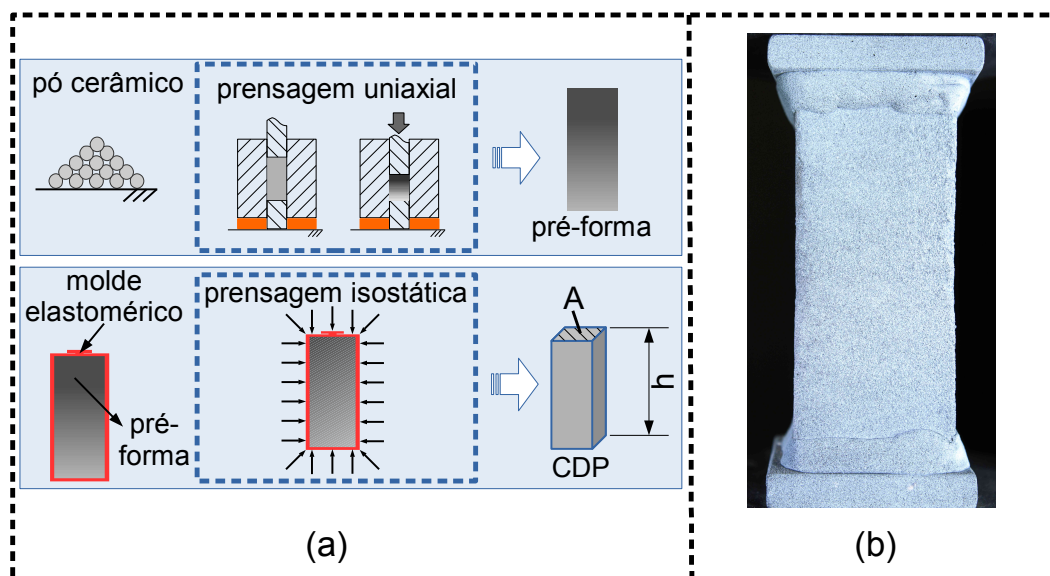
(a) Fabricação de CDPs para ensaios mecânicos de compressão simples e (b) fotografia de um CDP após a fixação em placas metálicas e pintura
